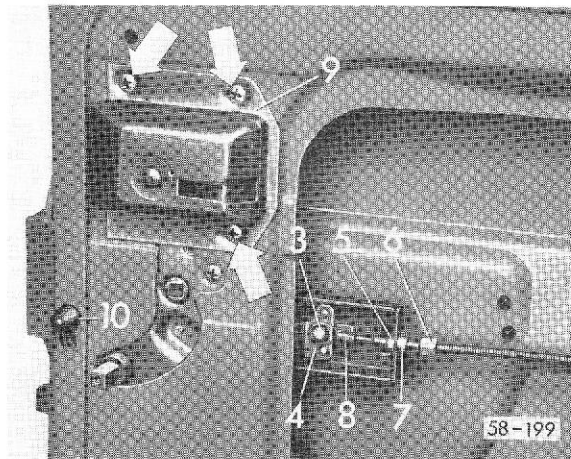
Démontage du câble Bowden/biellette, de la plaquette d'arrêt de porte et du bouton de sûreté
